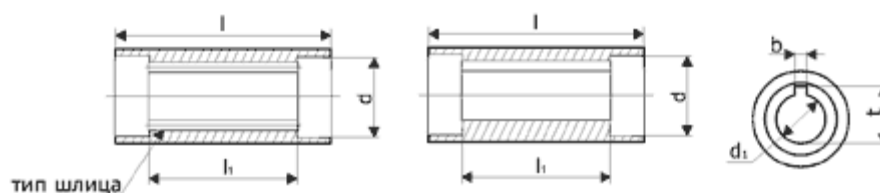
Приєднувальні розміри порожнистих валів редуктора 2Ч-63
